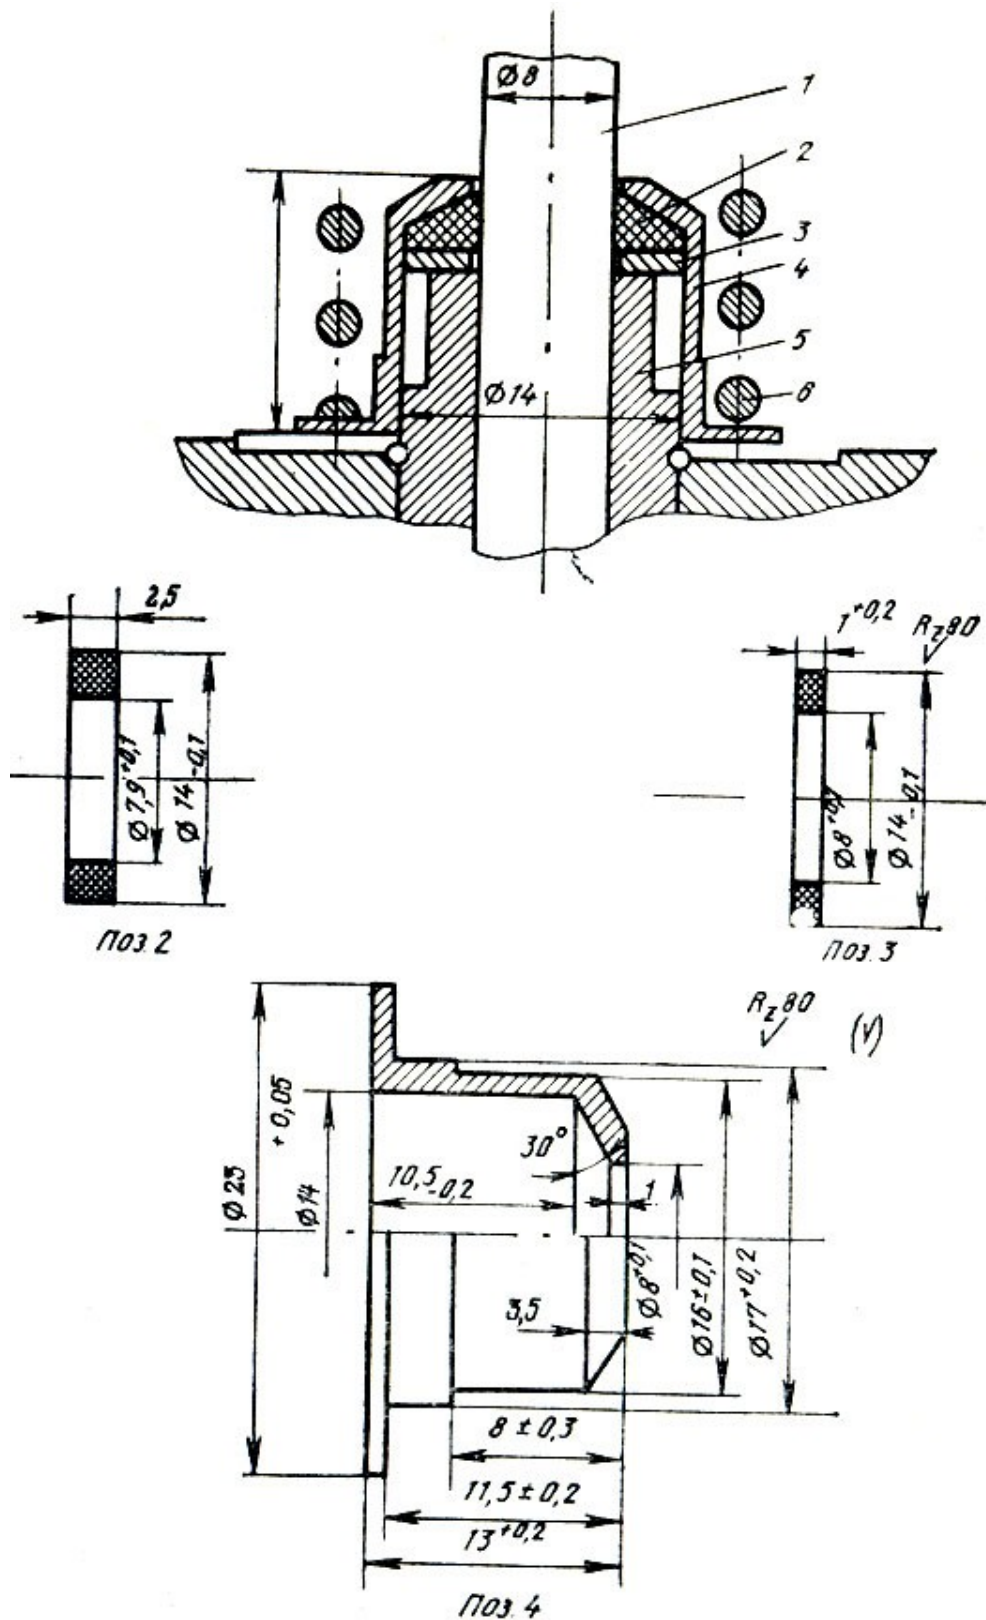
Уплотнение Л. Данилюка для стержня клапана: 1 — стержень клапана; 2 — кольцо (фторопласт Ф—4); 3 — шайба (сталь или бронза); 4 — колпачок (сталь или бронза); 5 — направляющая втулка; 6 — внутренняя пружина клапана
